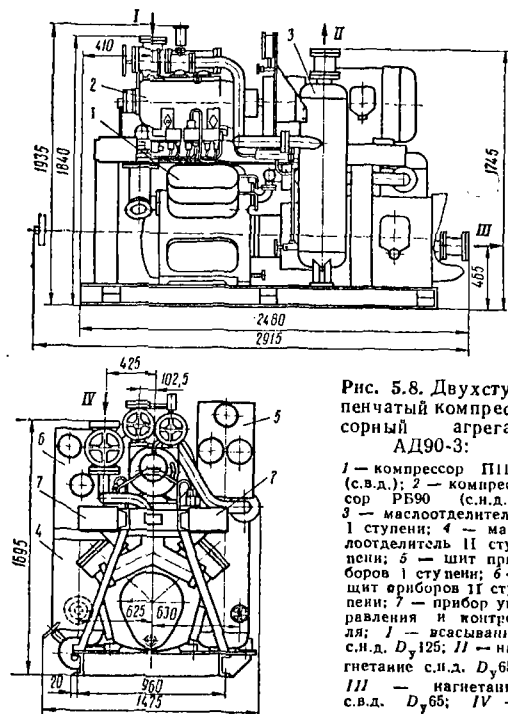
Двухступенчатый компрессорный агрегат АД90-3:
